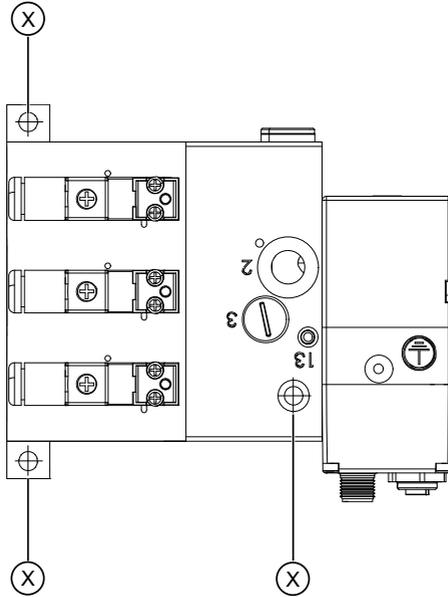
2- und 3-Gas-Standardausführung, Befestigung von oben, Durchgangsbohrung d 6,5
